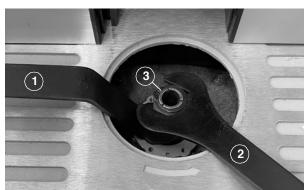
Installation und Wechsel der Werkzeugaufnahme
